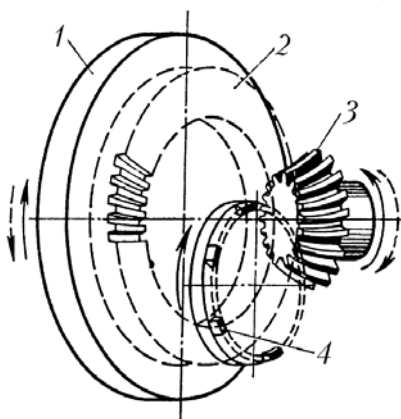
Нарізування конічних коліс із криволінійними зубами: 1 – інструментальний барабан, 2 – уявлюване виробляюче коло, 3 – нарізаємо зубчасте коло, 4 – зуборізна головка з різцями.
